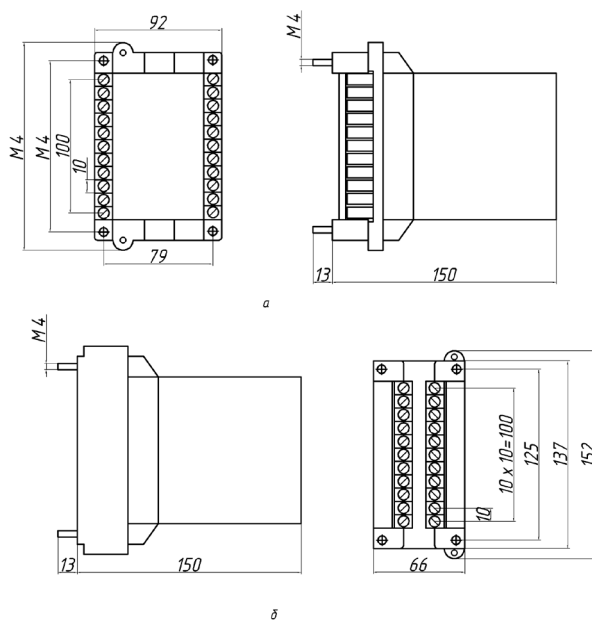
Габаритные размеры реле РТС-80 на базе основания СУРА-3
